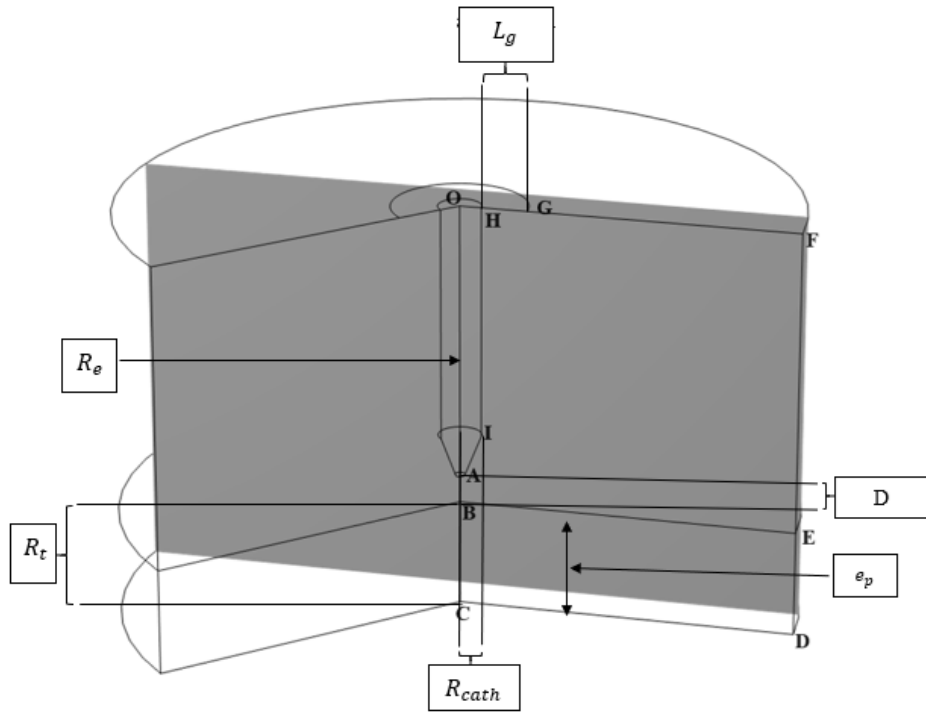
Géométrie (3D) de système soudure à TIG
